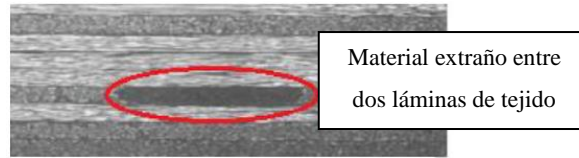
Defecto por inclusiones en el laminado. Extraído de [29].
